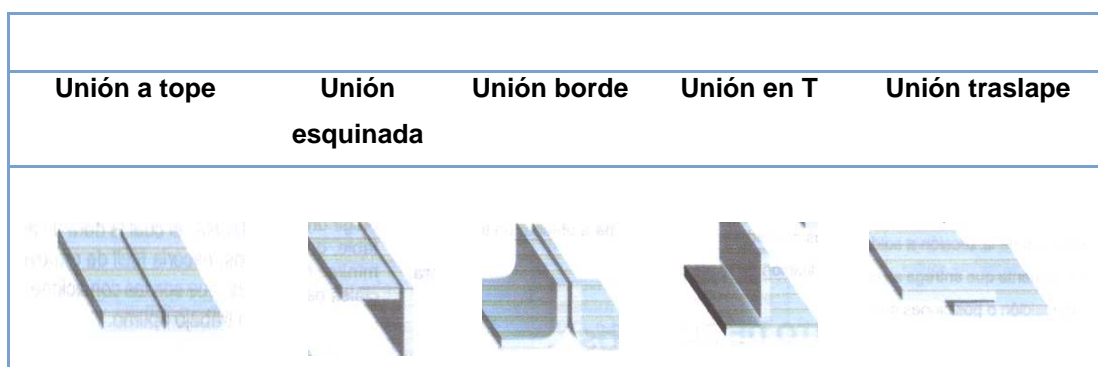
TIPOS DE UNIÓN DE SOLDADURA
